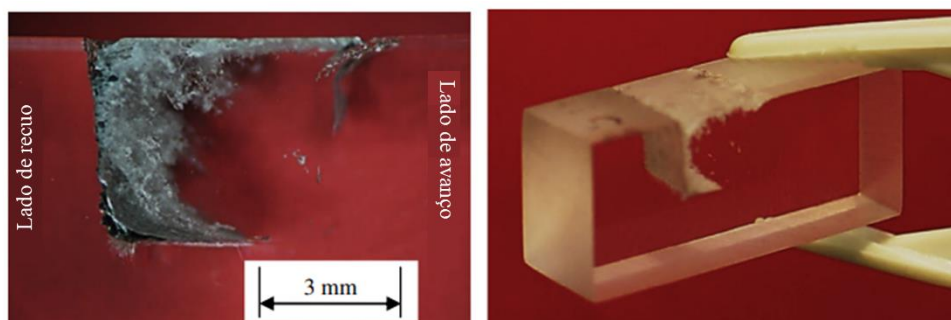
Corte transversal das amostras soldadas, adaptado de [21].
